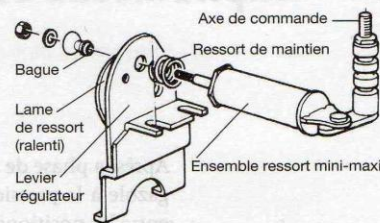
Régulateur mini-maxi CAV-Roto-Diesel
